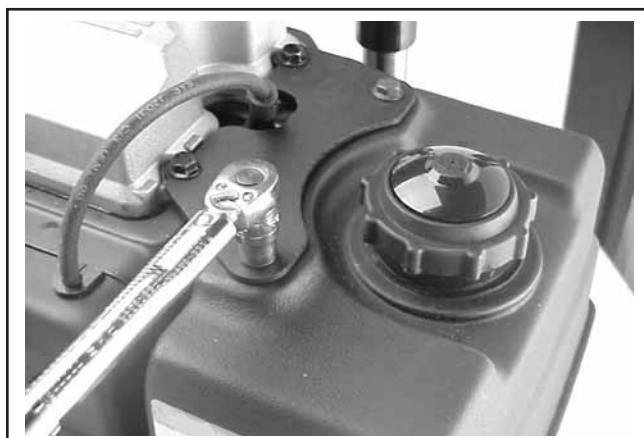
Installation des vis de montage supérieures du réservoir de carburant.
